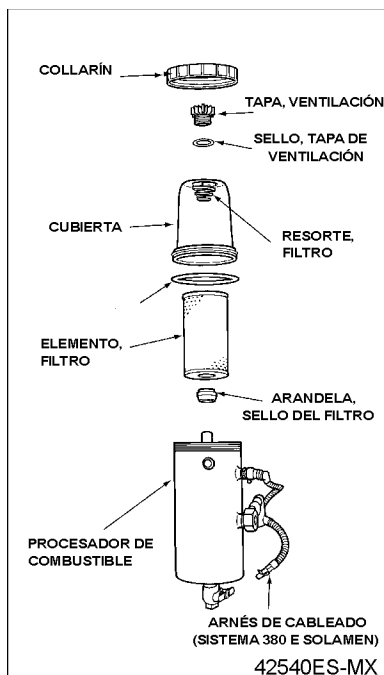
Ensamble del procesador de combustible Fuel Pro 382E
